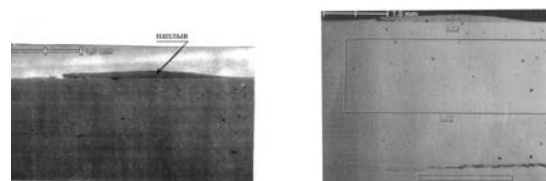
Включения корунда на поверхности исходной заготовки рабочей лопатки компрессора под слоем меди (до нагрева под выдавливание)
